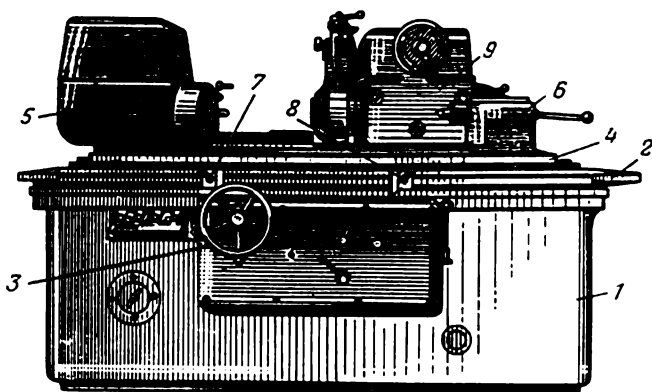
Vue d'ensemble d'une machine à rectifier cylindrique modèle 3151
